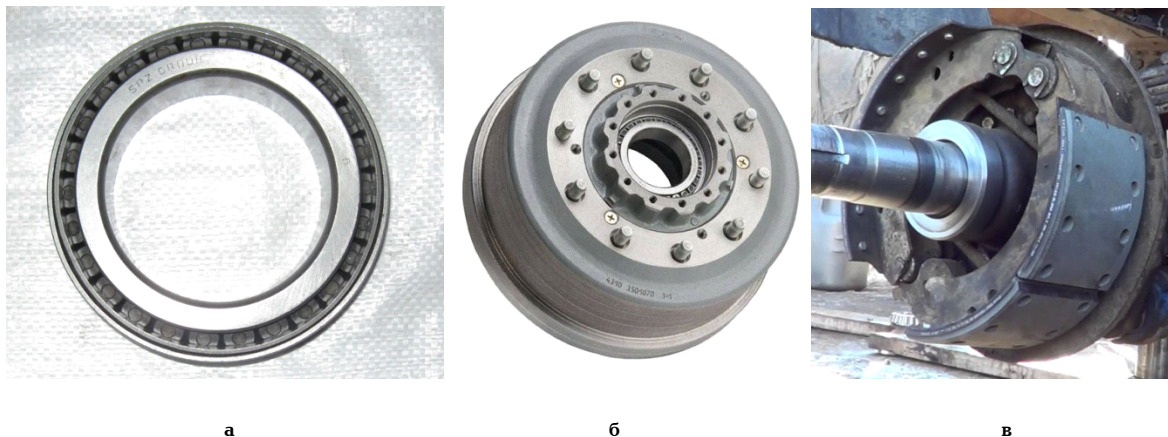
Внешний вид: а) подшипник 2007118А; б) ступица с тормозным барабаном; в) фланец с тормозными колодками
